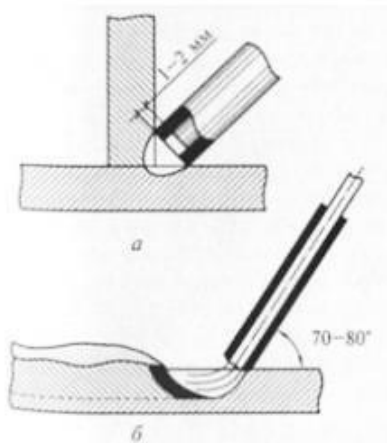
Сварка в глубоким проплавлением
